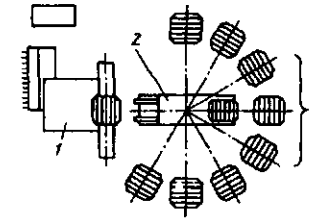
Гибкий производственный модуль со стендовым накопителем веерного типа: 1 – станок с ЧПУ; 2 – поворотный стол-перегрузатель; 3 – веерный накопитель заготовок, установленных на палетах
